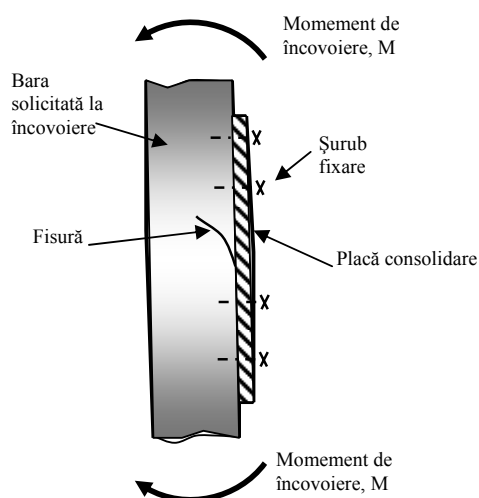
Schema de plasare pe bară a plăcuței pentru consolidare fisură
